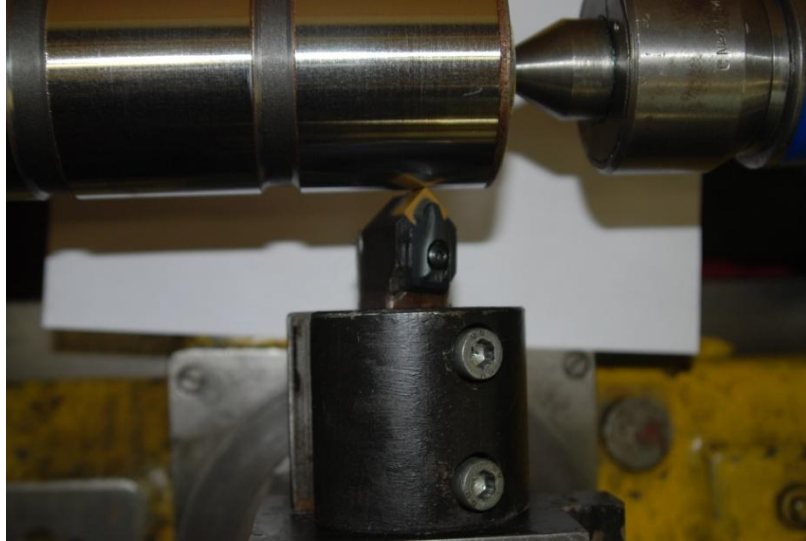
Установка СМП по схеме $Z_0X_0Y_1$, поворот вокруг оси OY против направления подачи (на угол ψ) [37].
